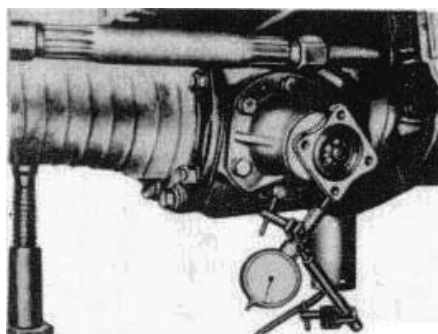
Проверка бокового зазора между зубьями шестерен главной передачи.
